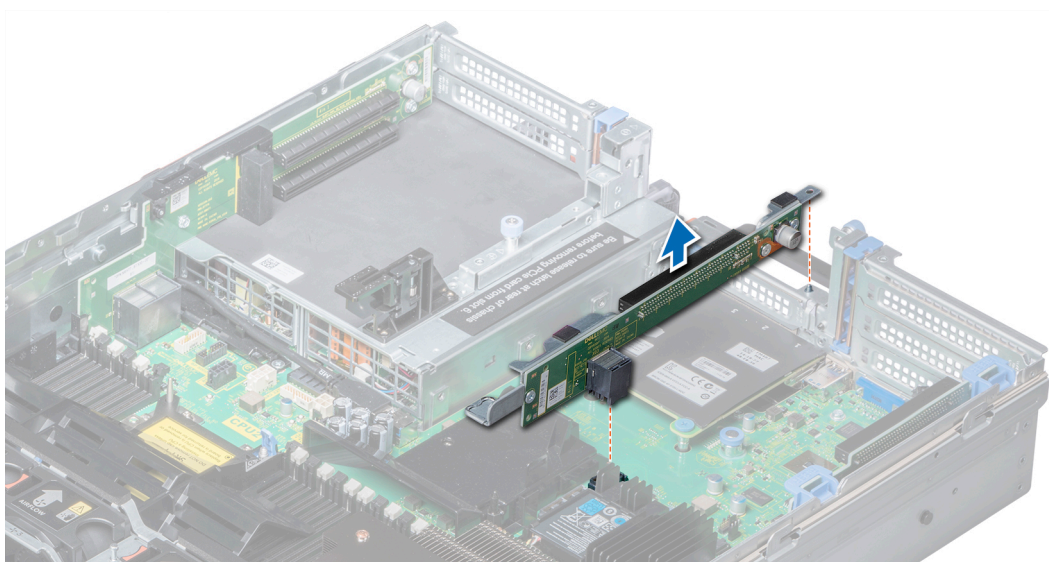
Retrait des cartes de montage pour carte d'extension 2
